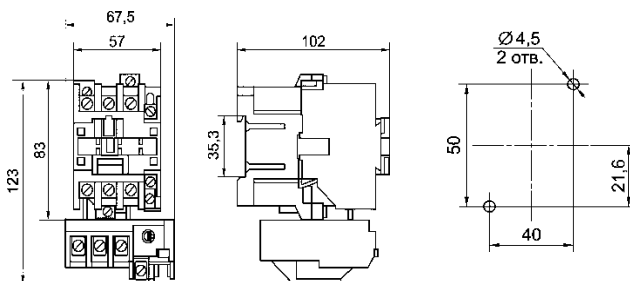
Пускатель неререверсивный ПМ12-025 25А. Степень защиты - IP00; IP20.
